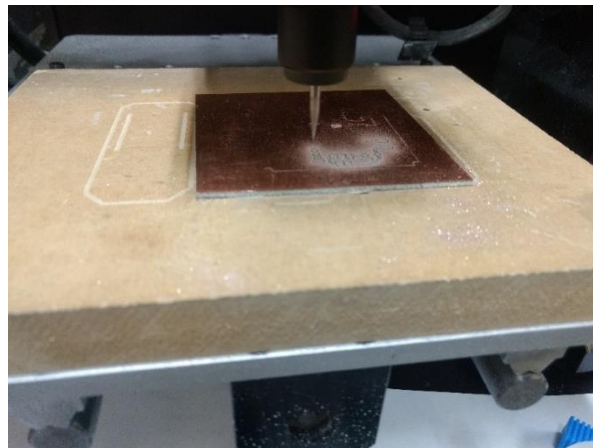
Proceso de manufactura de la placa impresa, con una máquina de control numérico.
